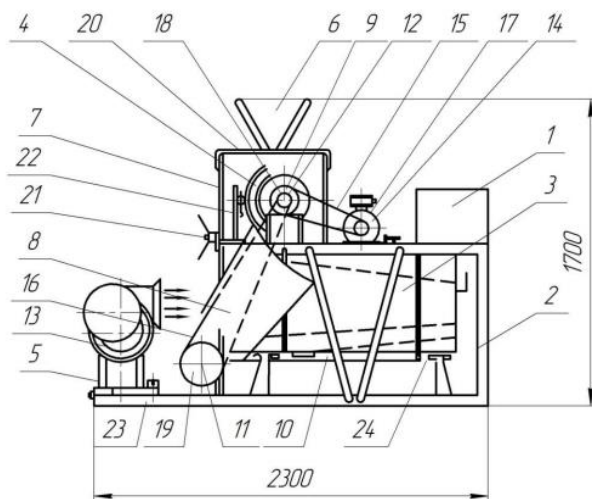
Загальний вид установки для лушення зерна: 1 - пульт керування; 2 - станина; 3 - ситовий кузов; 4 - прорезинена дека; 5 - рама вентилятора; 6 - приймальний бункер; 7 - лущильна камера; 8 - захисний кожух; 9 - абразивний барабан; 10 - тяга; 11 - ексцентриковий механізм; 12 - шків робочого барабану; 13 - вентилятор; 14 - електродвигун приводу робочого барабану; 15 - клинопасова передача робочого барабану; 16 - клинопасова передача ексцентрикового механізму; 17 - привідний шків; 18 - підшипникові опори; 19 - шків ексцентрикового механізму; 20 - засувка регулювання подачі зерна; 21 - регулювальний гвинт; 22 - кронштейн механізму регулювання робочого зазору; 23 - кріплення вентилятора; 24 - обмежувачі руху ситового кузову
